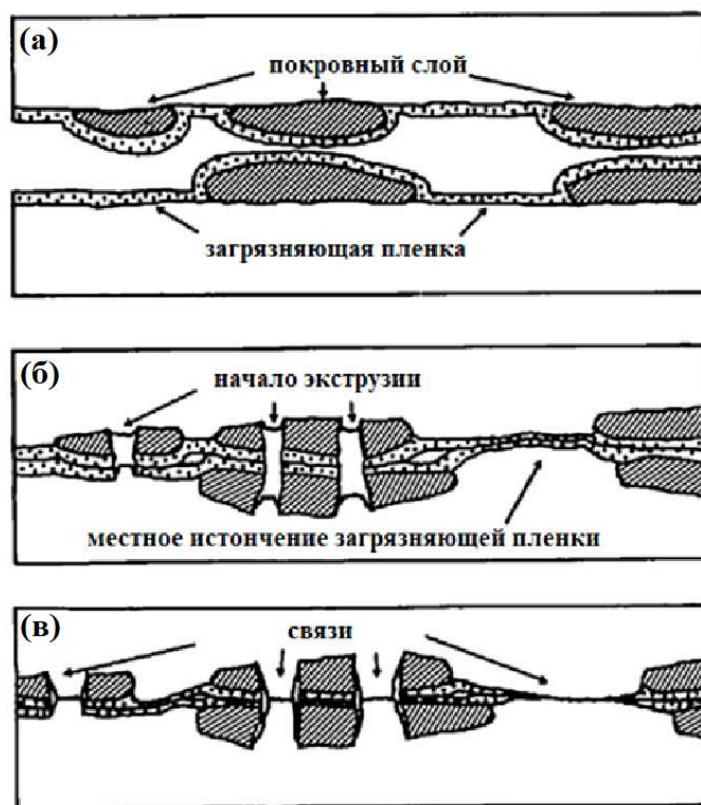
Модель соединяющего механизма при холодной сварке [55]
